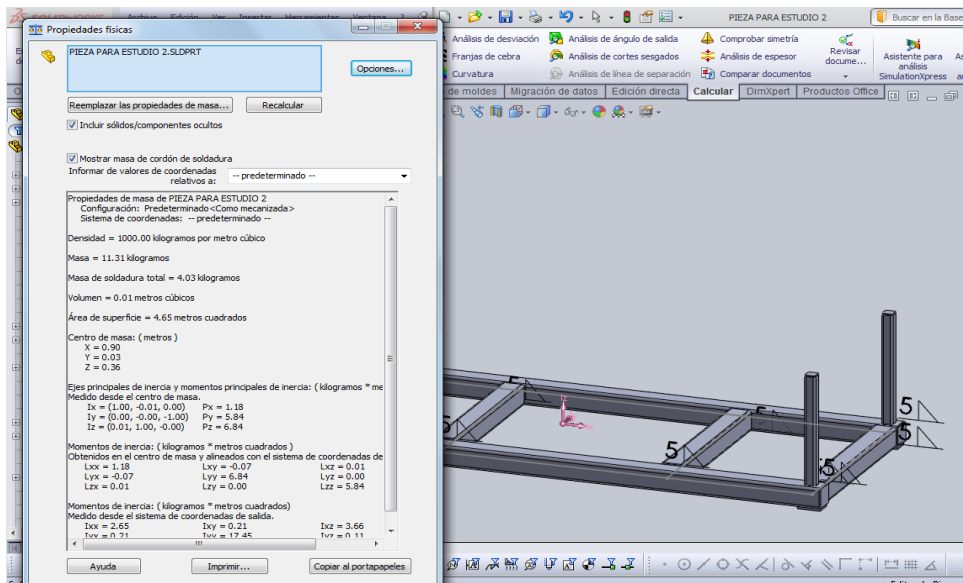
Cálculo de masas y dimensiones de la estructura
